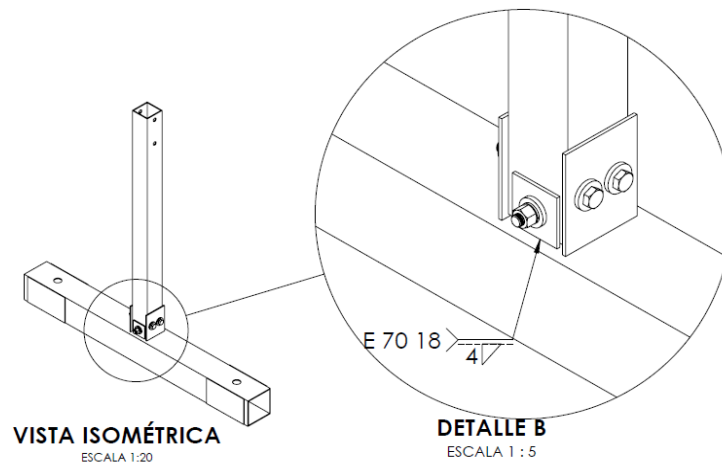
Soldadura a filete en una sola cara con lado efectivo de 4 mm
